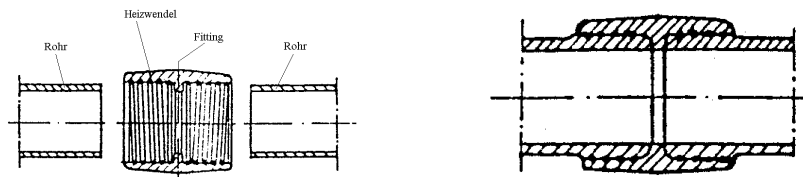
Heizwendelschweißen von Muffen
